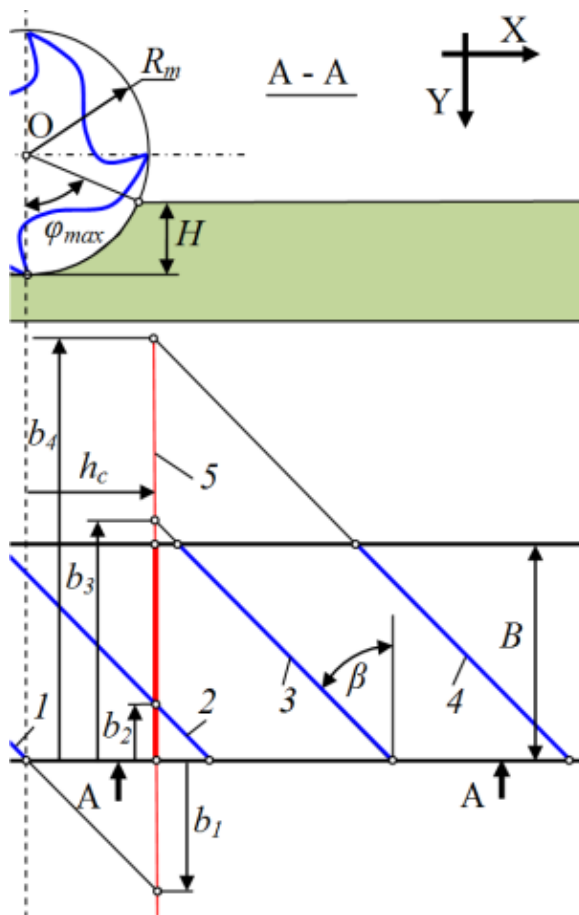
Схема для визначення геометричного зачеплення зубів фрези та заготовки [85]
